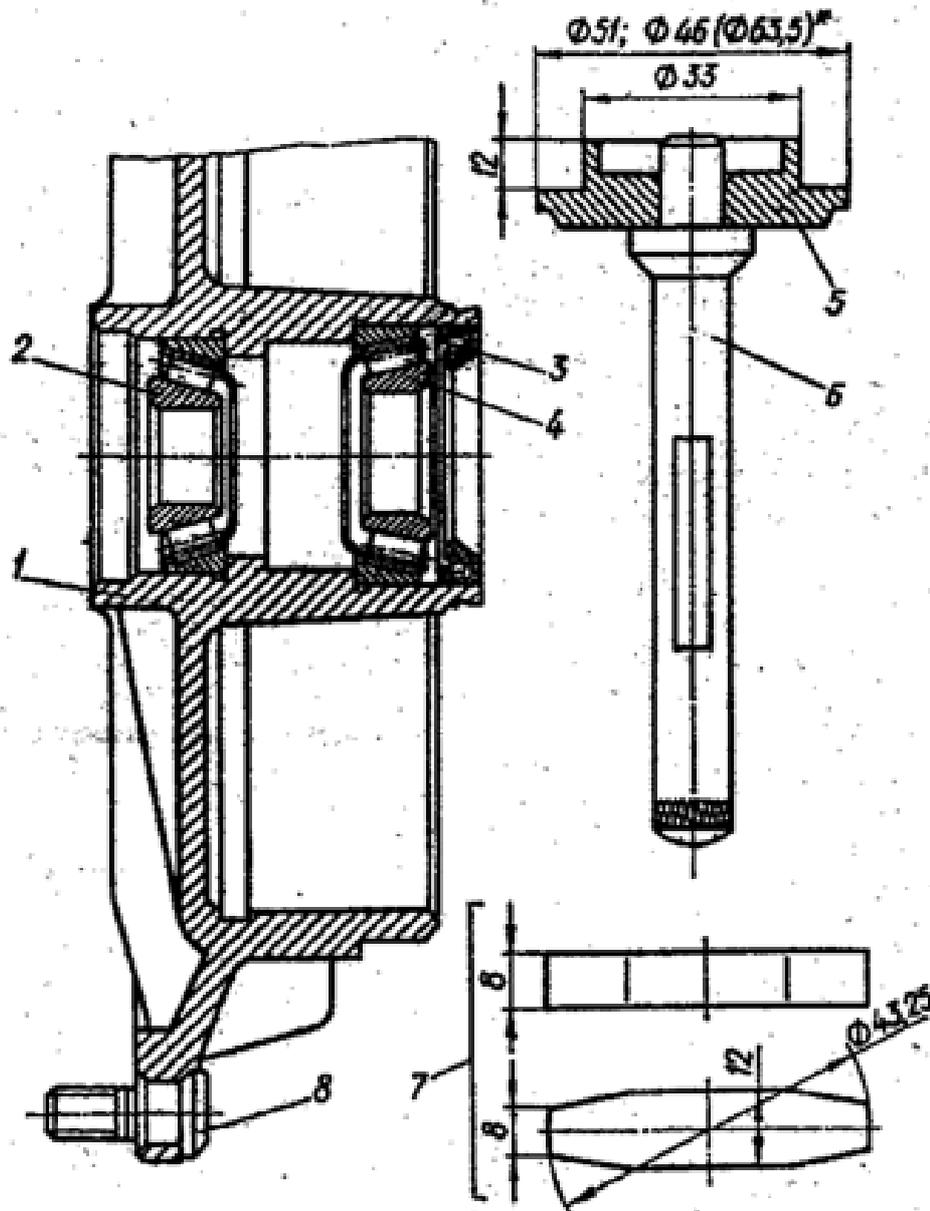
Тормозной барабан заднего колеса в сборе и оправки: 1 - барабан тормозной; 2 - подшипник наружный; 3 - манжета уплотнительная; 4 - подшипник внутренний; 5 - оправка для запрессовки колец подшипников и манжеты: (*размер $\varnothing 63,5$ мм дан для подшипника ступицы переднего колеса); 6 - ручка оправки; 7 - оправка для выпрессовки наружного кольца внутреннего подшипника; 8 - болт крепления колеса
